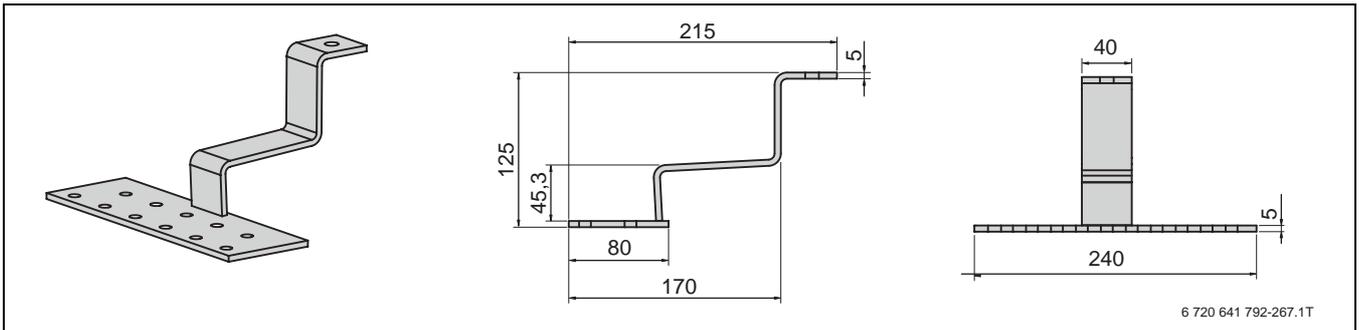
Collegamento da tetto per Logasol SKR con coperture con tegole, tegole in laterizio ed embrici
